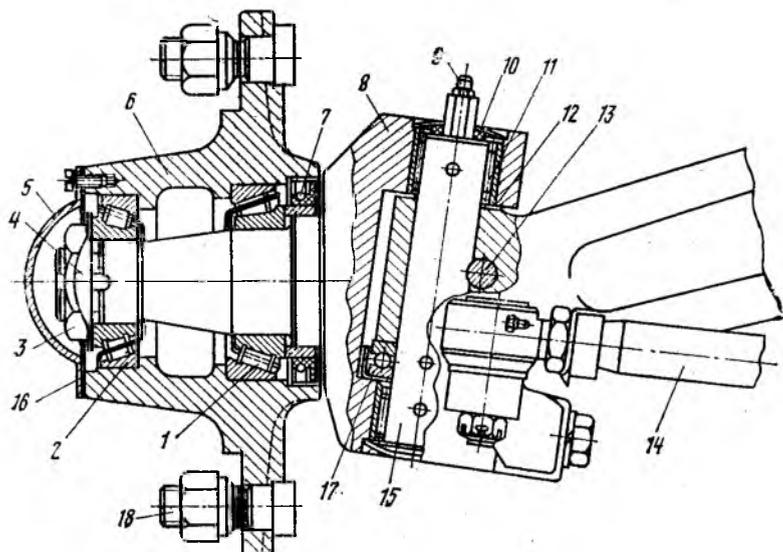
Установка поворотного кулака погрузчика Ф17.ДУ32.33.1:
